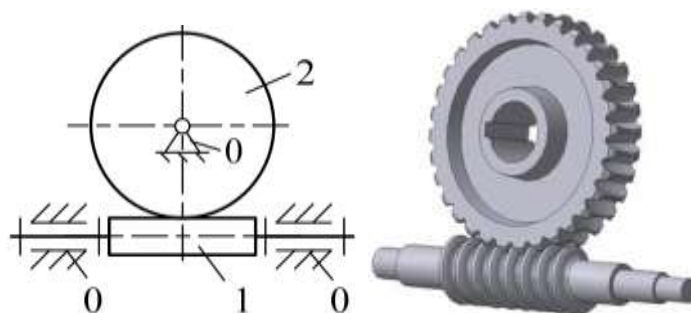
Зубчатые передачи со скрещивающимися осями
